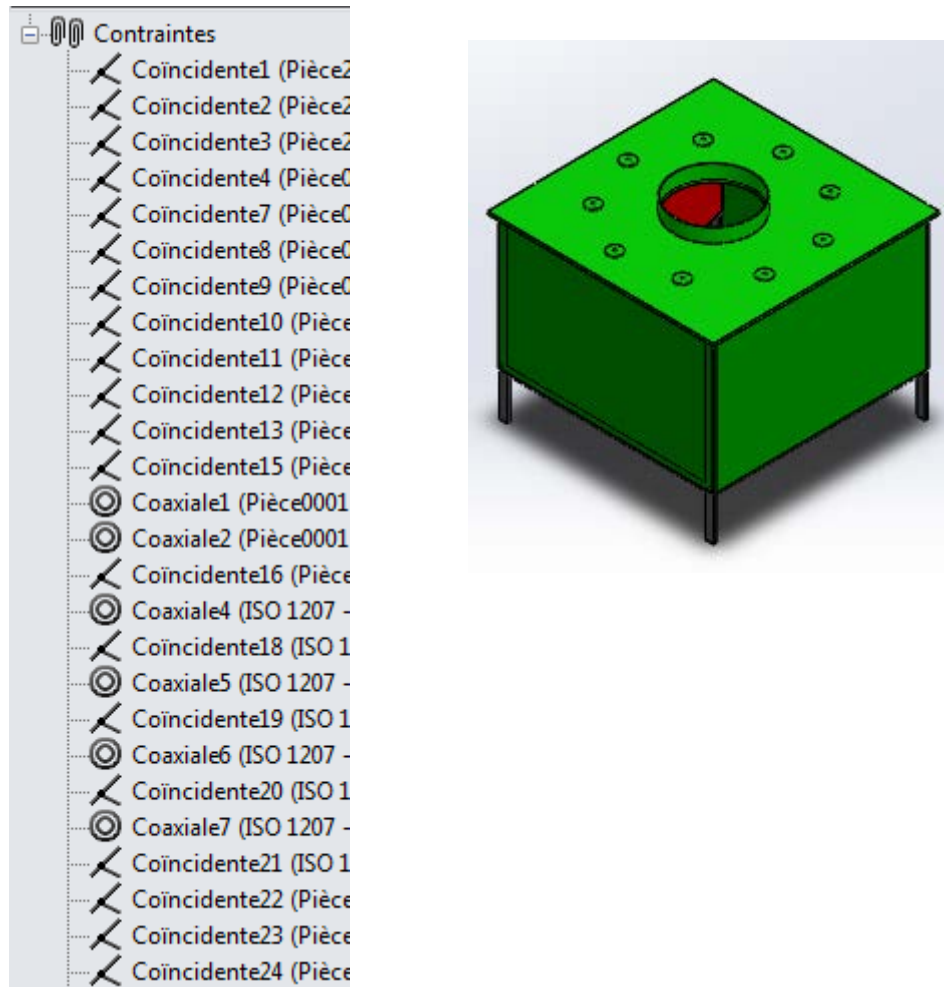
Les composantes du sous assemblage 1 dans une seule zone graphique
